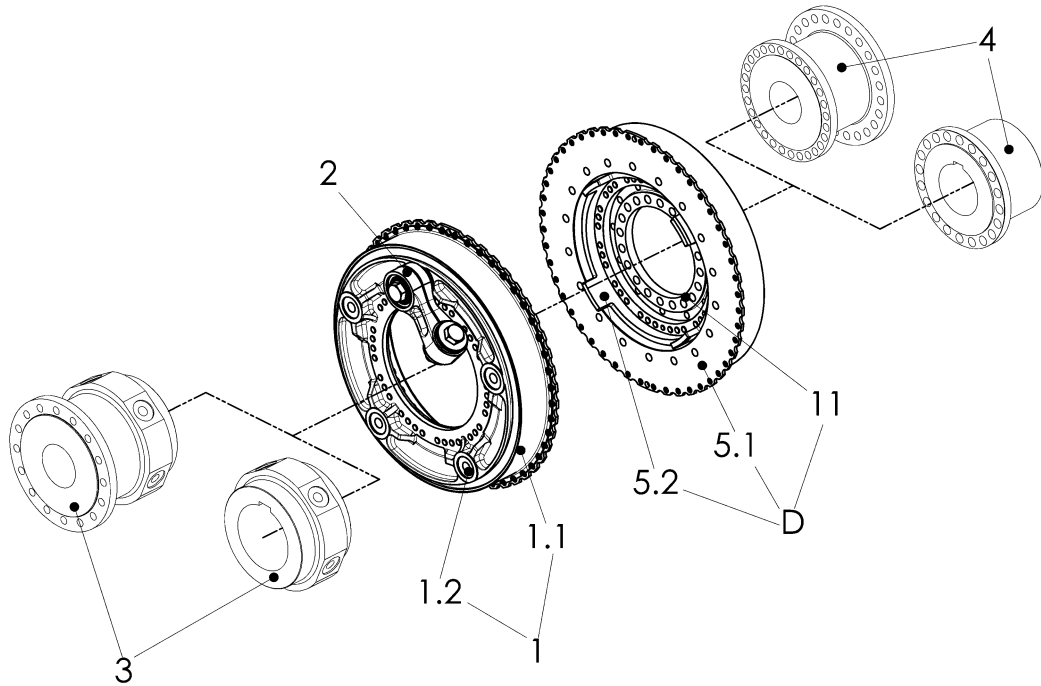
Beispiel: 016L-00050...00080 und 00082...00090-..20
